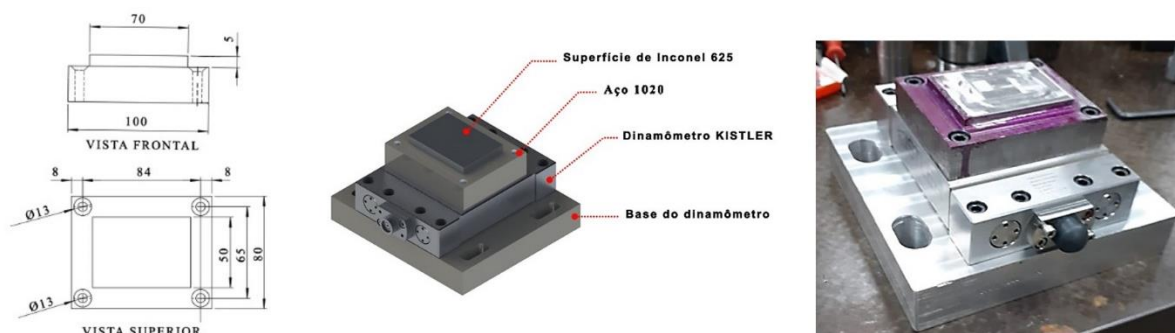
Configuração esquemática dos corpos de prova (CP) para os ensaios de fresamento do Inconel 625. À esquerda as dimensões do CP; no centro o CAD da montagem do conjunto CP-dinamômetro sobre a base para fixação na mesa do centro de usinagem; e à direita o CP fabricado e fixado por parafusos no dinamômetro.
